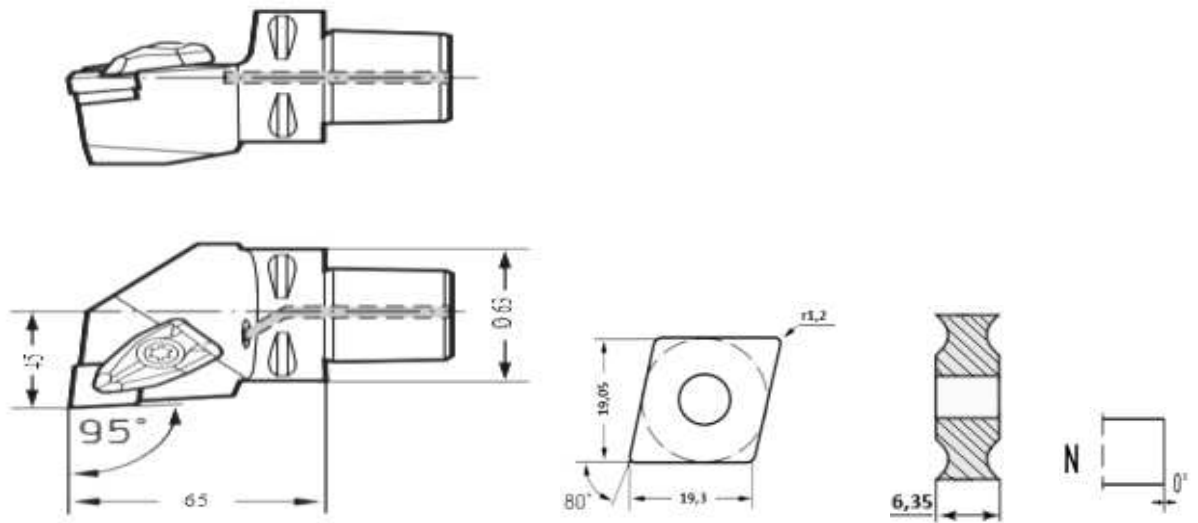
Державка C6-DCLNR-45065-19, пластина CNMG 190612-NM6
